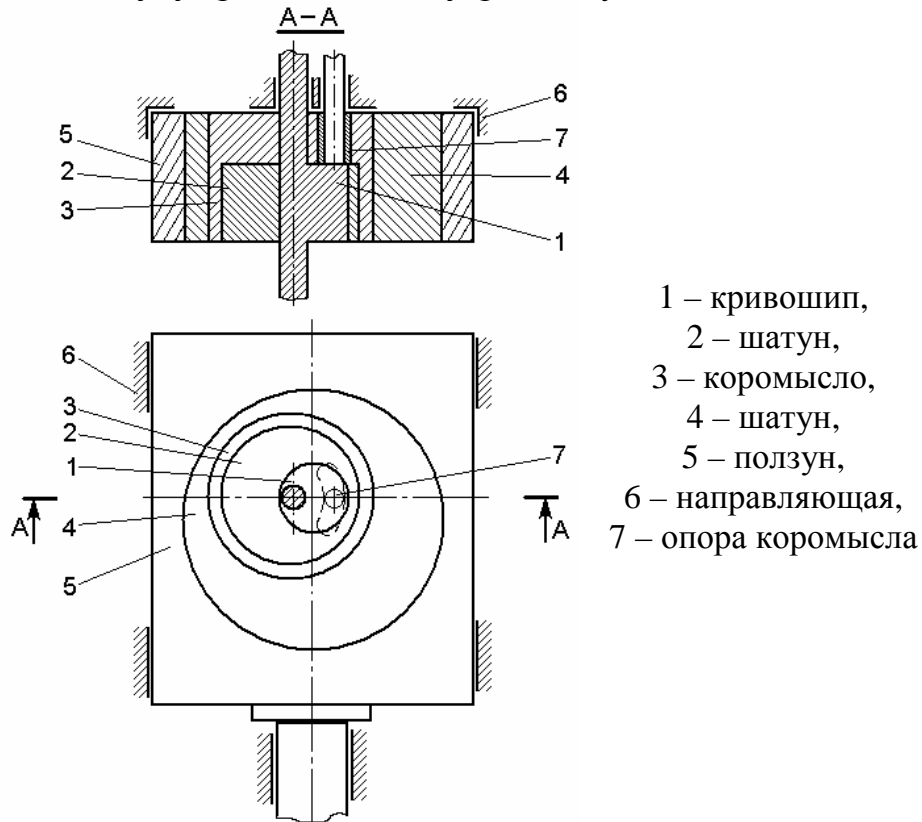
Конструктивная схема шестизвенного механизма с круговыми звеньями
